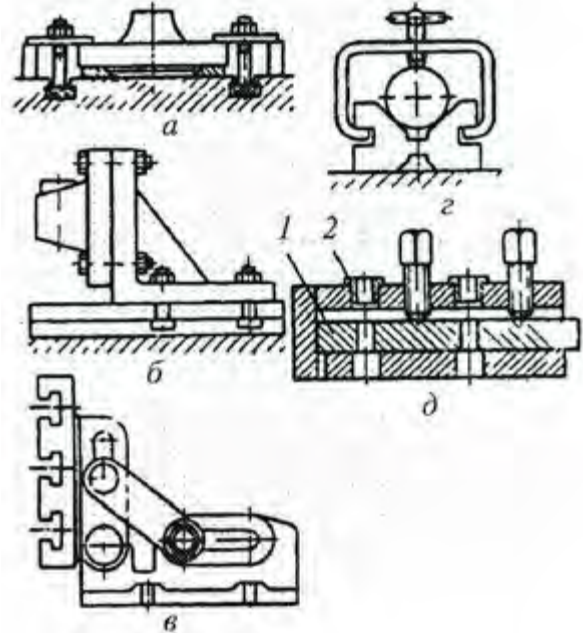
Пристрої для закріплення заготовок на свердильних верстатах
